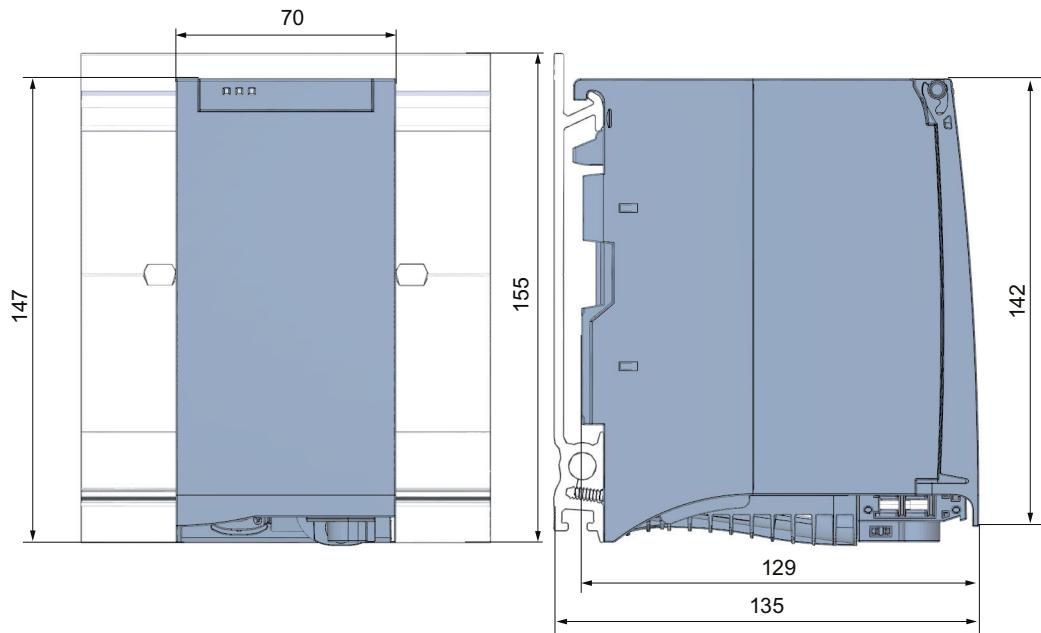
Габаритный чертеж блока питания PS 60W 24/48/60VDC
